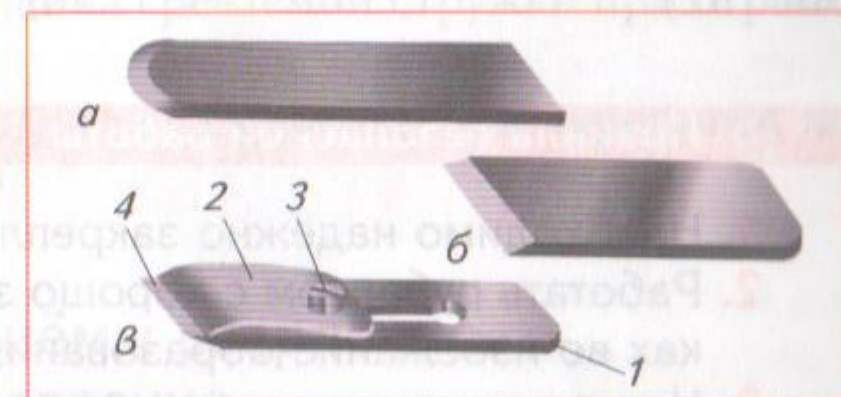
Ножи: а — шерхебеля; б — рубанка и фуганка; в — рубанка и фуганка со стружколомателем: 1 — нож; 2 — стружколоматель; 3 — болт с гайкой; 4 — режущая кромка ножа
